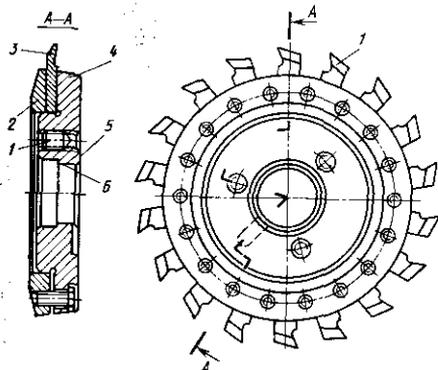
Резцовая головка для нарезания прямозубых конических колес
